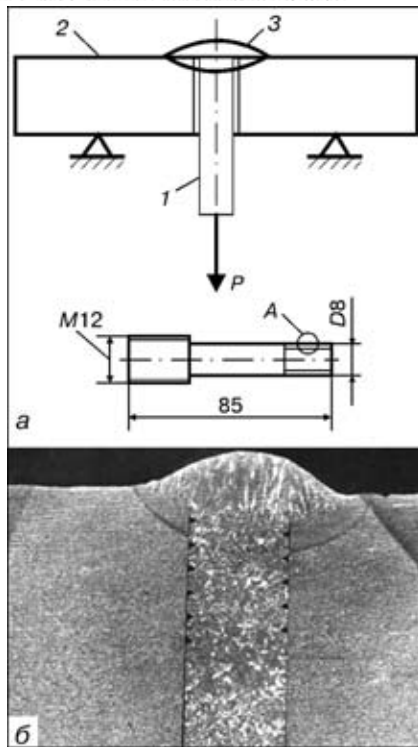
Схема испытания по методу Имплант и вид образца (а): 1 – образец; 2 – пластина; 3 – шов; P – нагрузка, а также макрошлиф соединения (б)
